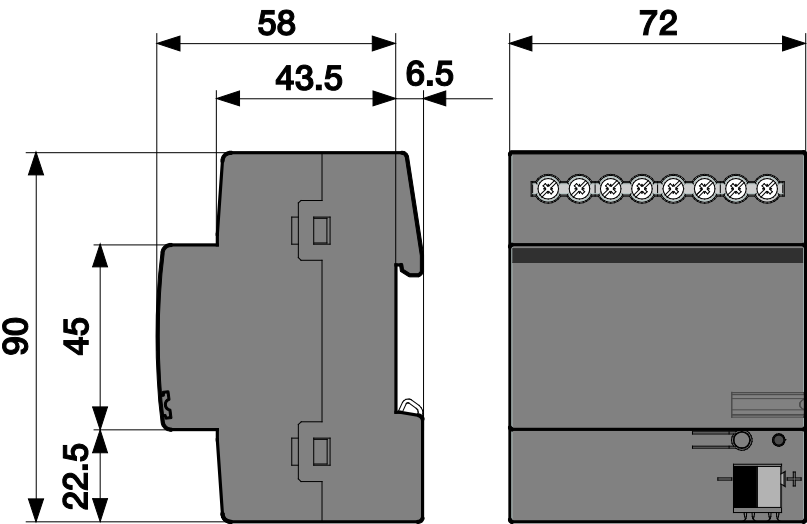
Dimensões atuador de aquecimento 6 vezes
